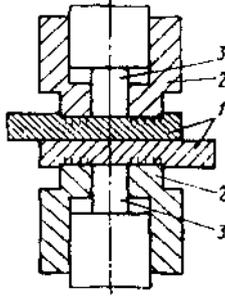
Схема сварки с предварительным зажатием свариваемых деталей.
